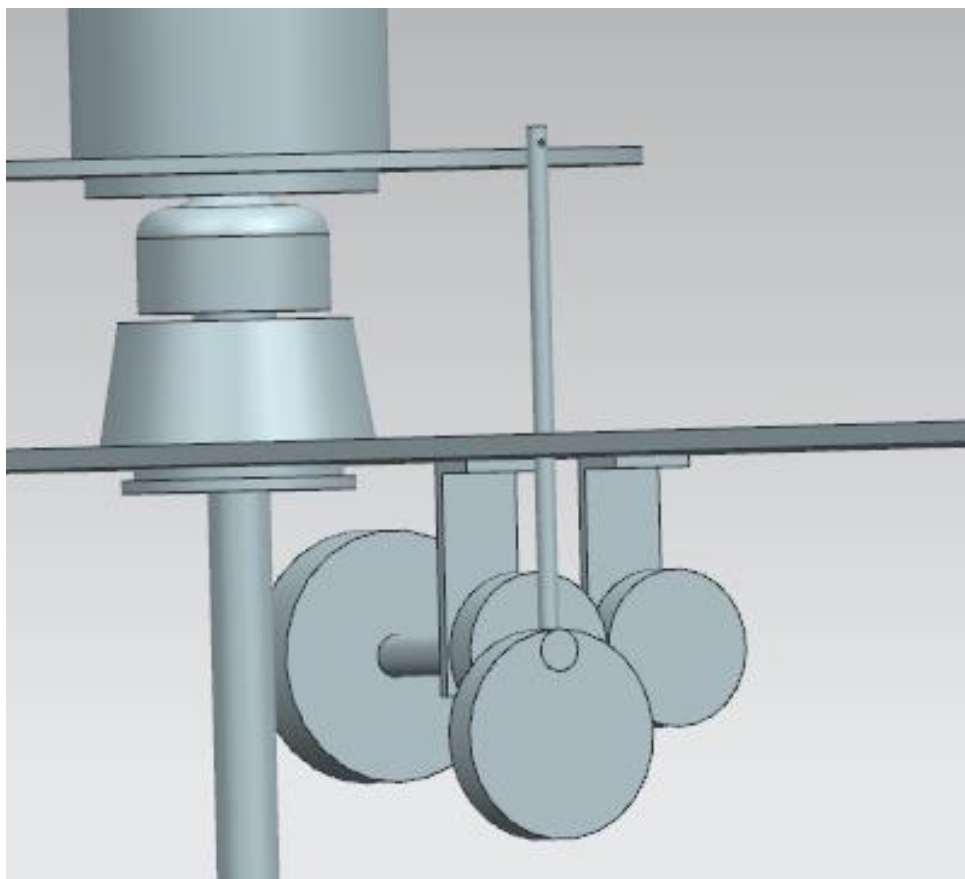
Цилиндрическая передача и кулачковый механизм намоточного устройства
